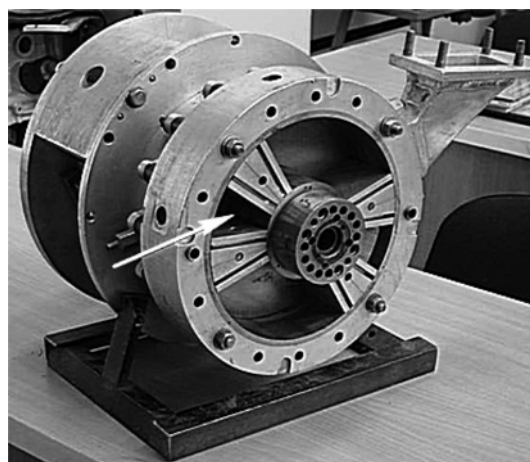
Общий вид преобразующего механизма роторно-лопастного двигателя
